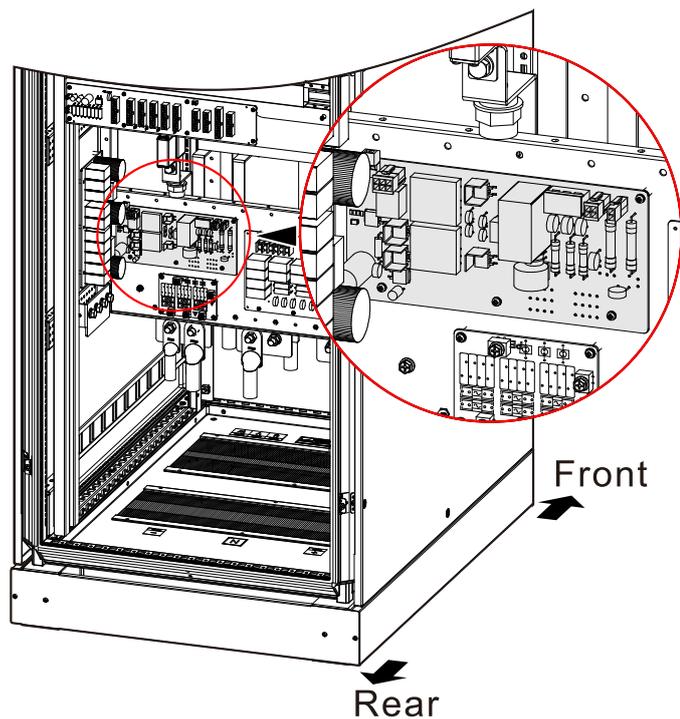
Установка платы устройства управления размыкателем цепи батареи (вид на шкаф ИБП сзади)
